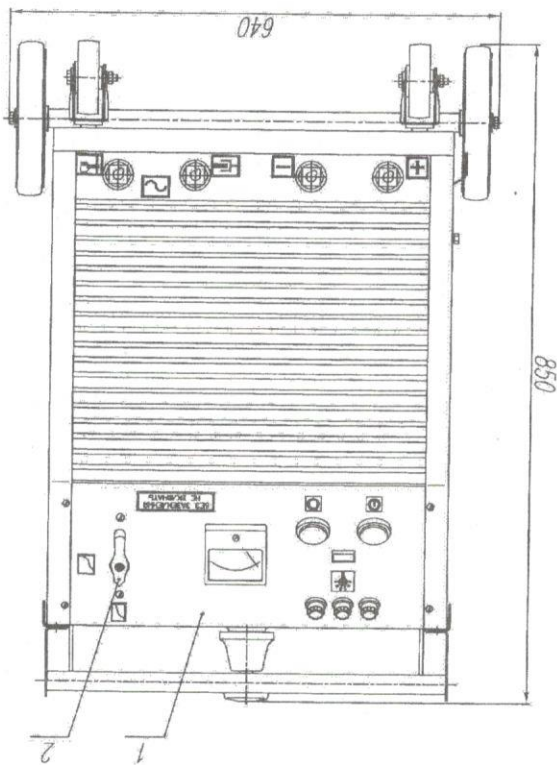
Общий вид выпрямителя сварочного ВД-405УЗ.
